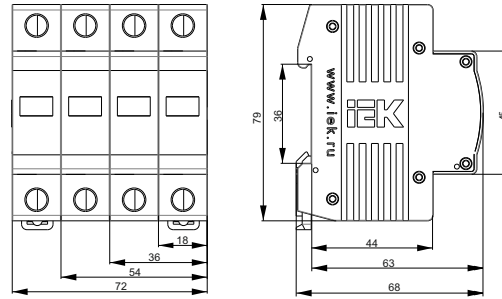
Габаритные и установочные размеры (мм) / Figure 3 – Overall and mounting dimensions (mm)
